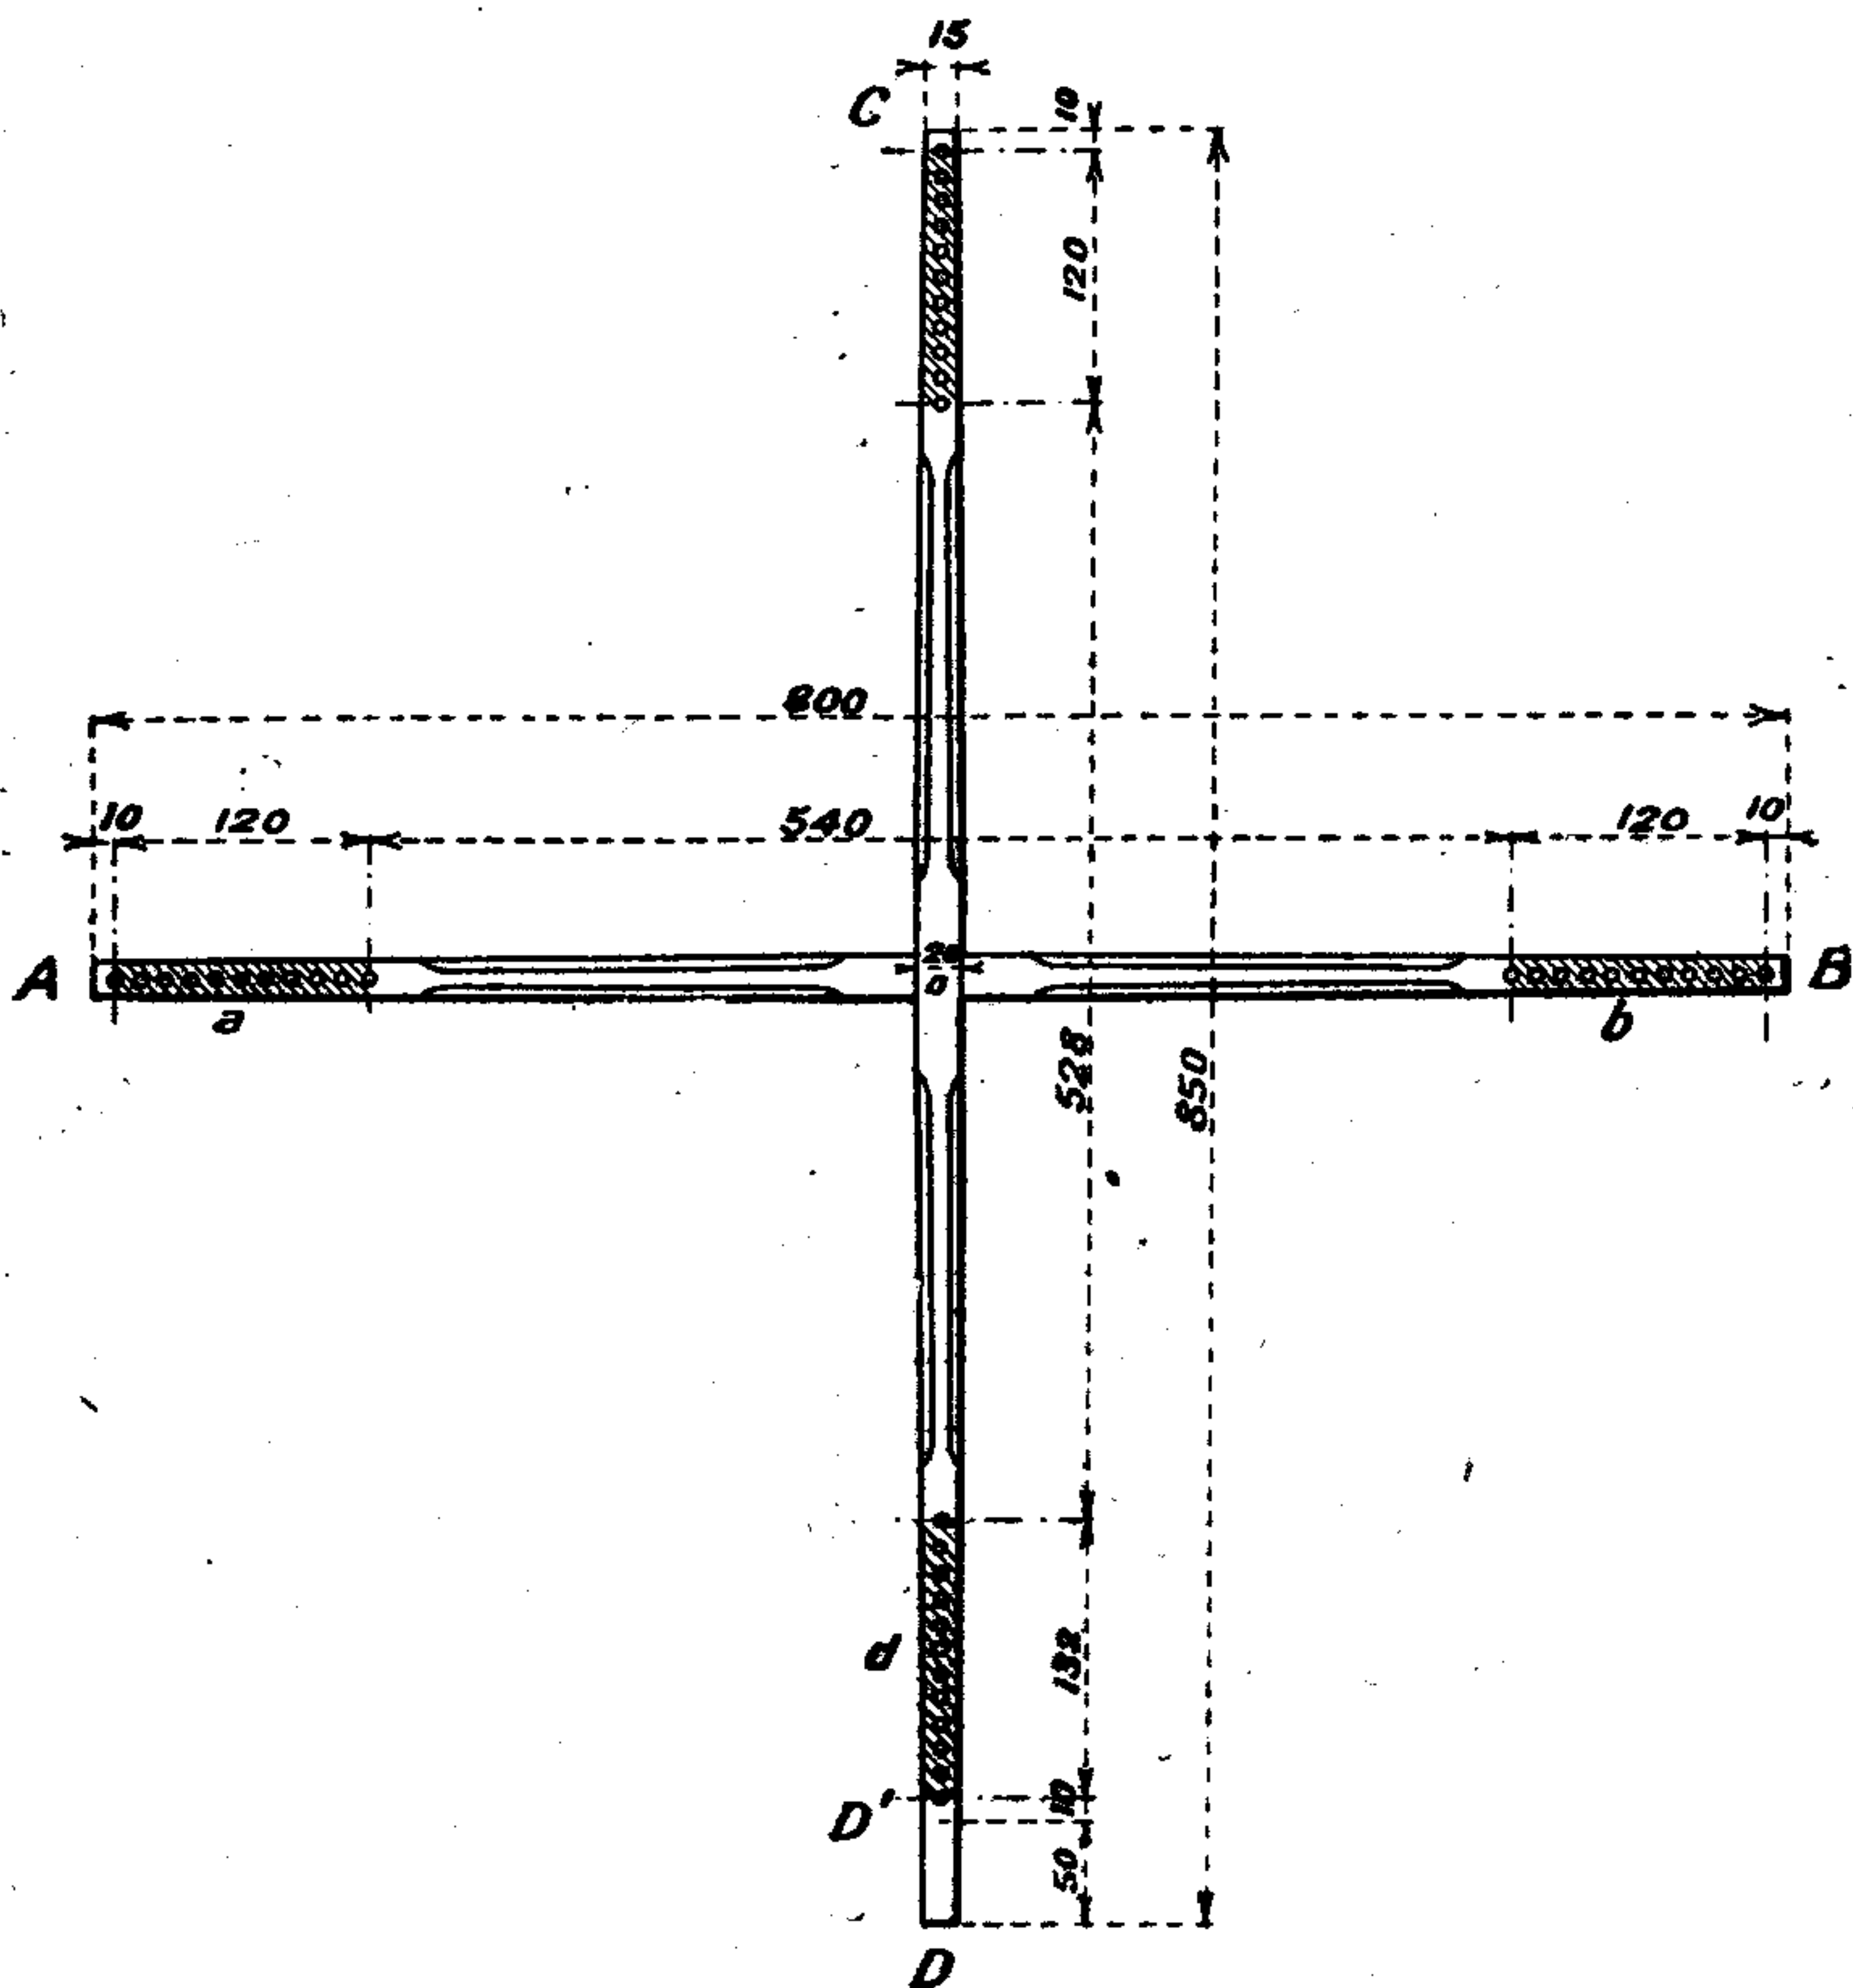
Carcasse de bois servant à la construction du cadre à quatre enroulements.
